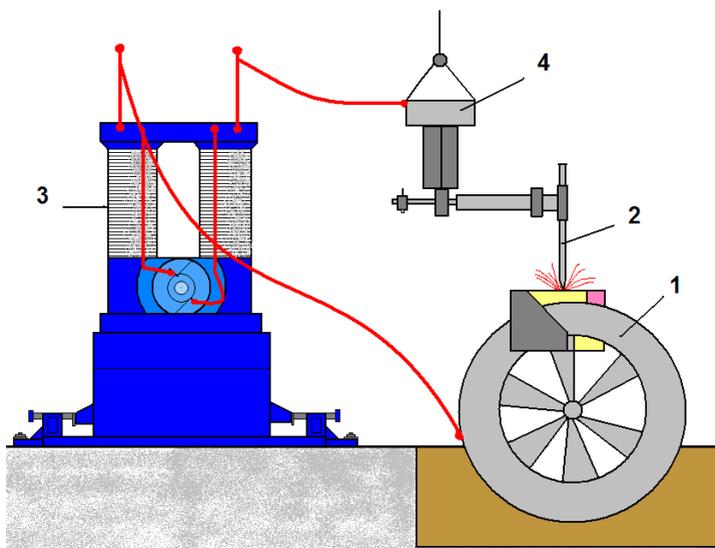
Сварочная установка, разработанная Н.Г. Славяновым
